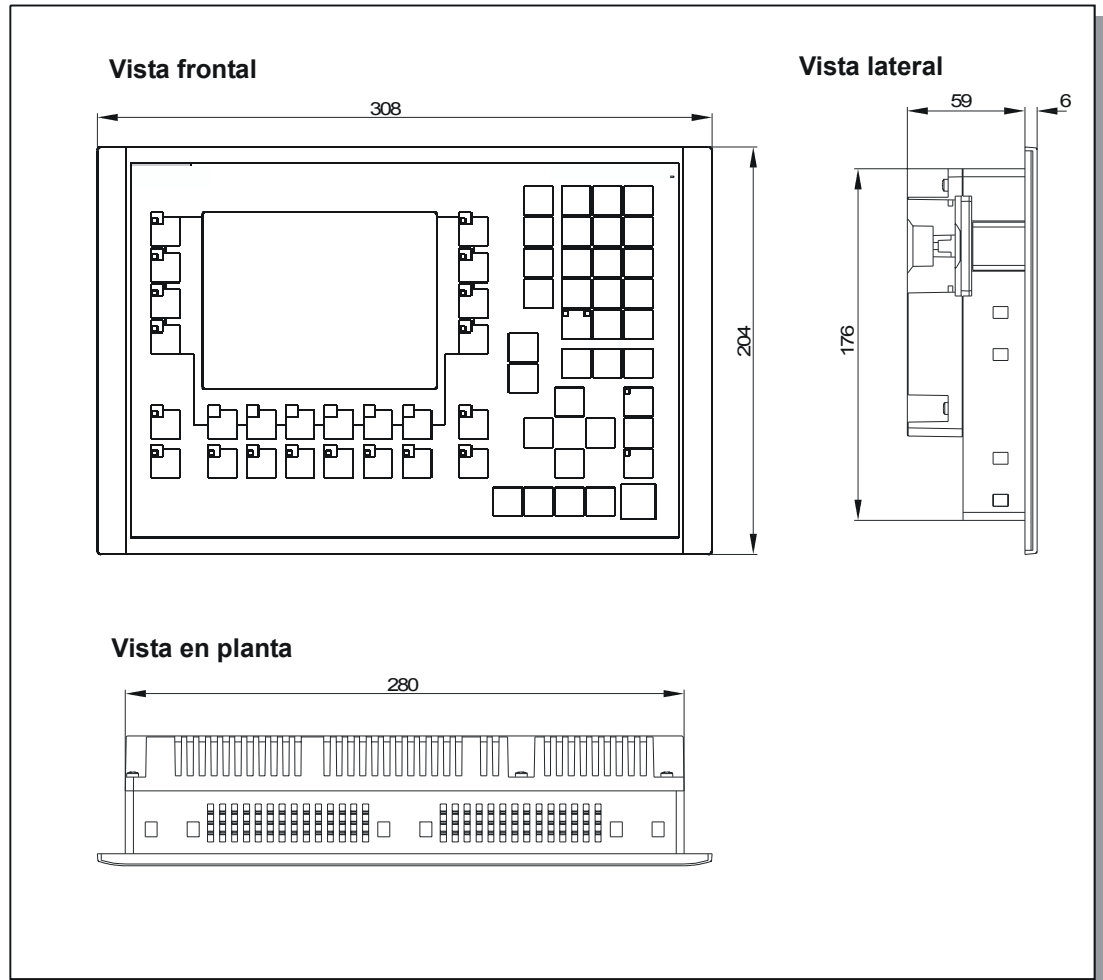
Dimensiones del panel de operador OP 270 6"
